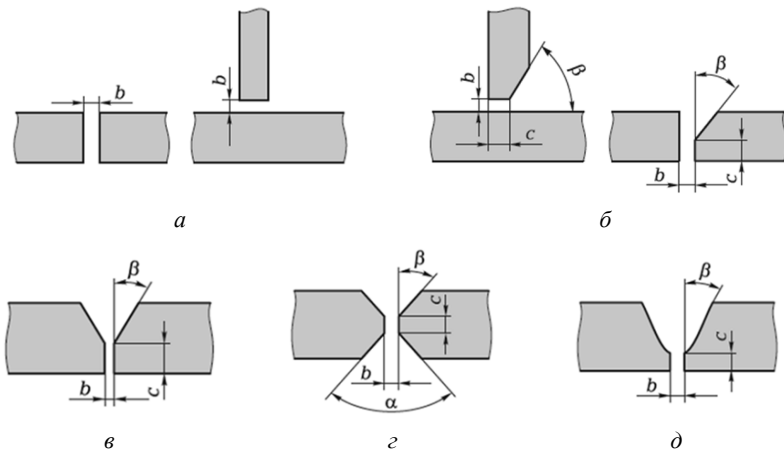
Конструктивные элементы разделки кромок под сварку:
